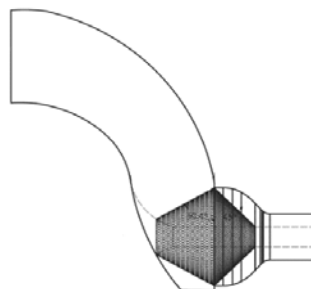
Конструкция нового углового входного патрубка осевого компрессора с объемным гасителем неравномерности
